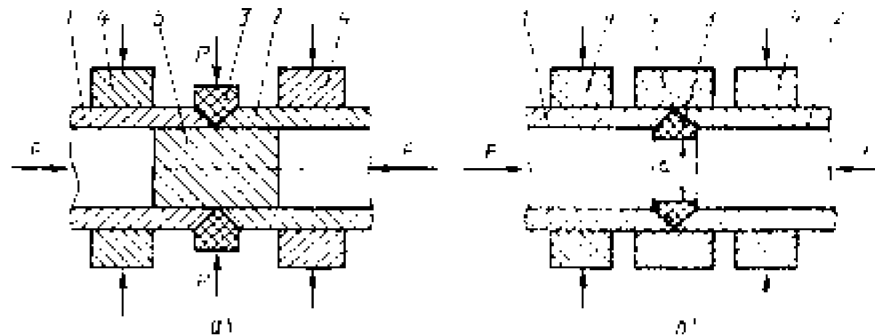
Схема радиальной сварки трением:
